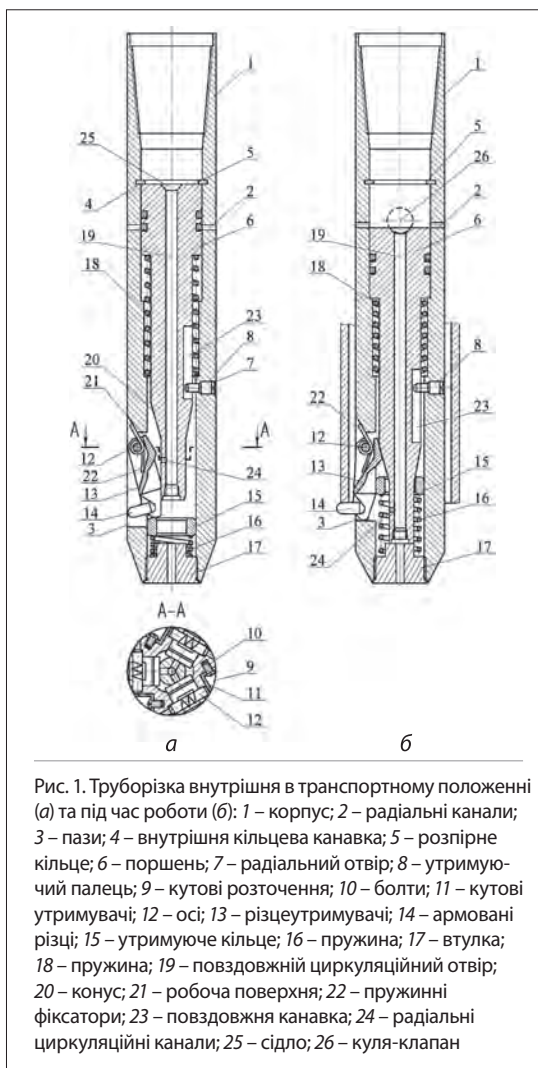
Труборізка внутрішня в транспортному положенні (а) та під час роботи (б): 1 – корпус; 2 – радіальні канали; 3 – пази; 4 – внутрішня кільцева канавка; 5 – розпірне кільце; 6 – поршень; 7 – радіальний отвір; 8 – утримуючий палець; 9 – кутові розточення; 10 – болти; 11 – кутові утримувачі; 12 – осі; 13 – різцеутримувачі; 14 – армовані різці; 15 – утримуюче кільце; 16 – пружина; 17 – втулка; 18 – пружина; 19 – повздовжній циркуляційний отвір; 20 – конус; 21 – робоча поверхня; 22 – пружинні фіксатори; 23 – повздовжня канавка; 24 – радіальні циркуляційні канали; 25 – сідло; 26 – кулі-клапан
